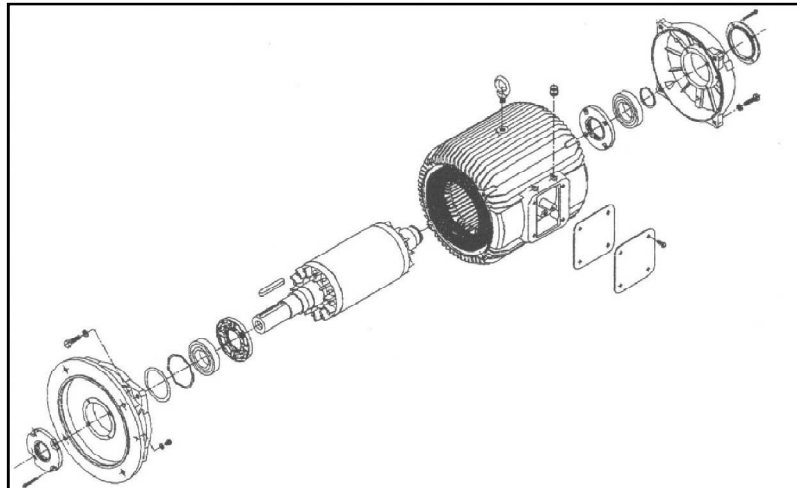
Despiece de un motor asíncrono trifásico con rotor de jaula de ardilla.
